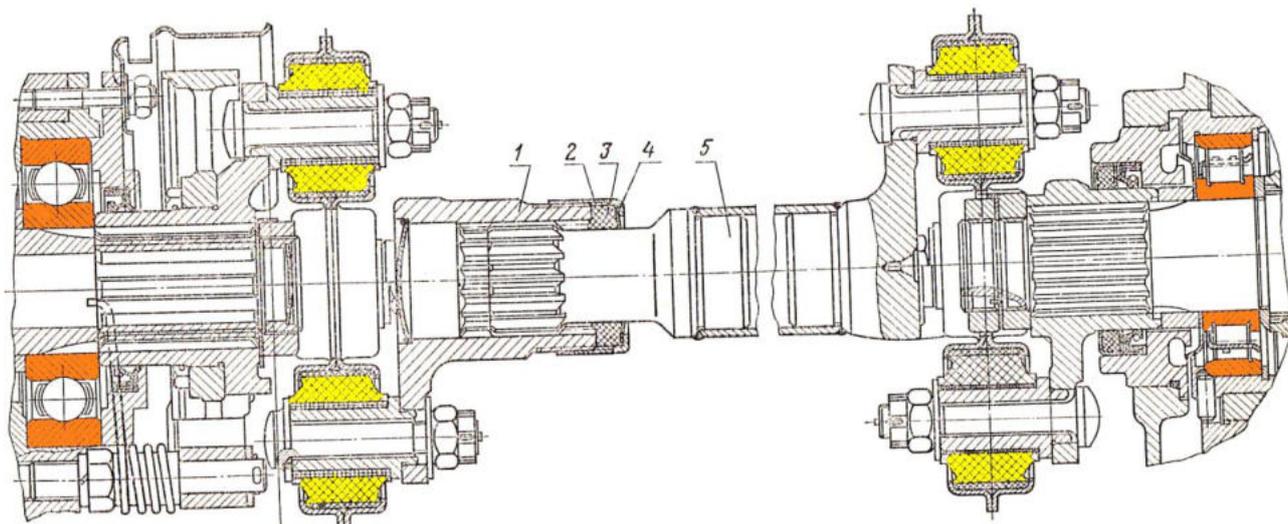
Карданная передача тракторов ДТ-75М, ДТ-75Б, ДТ-75К без УКМ, ходоуменьшителя и реверс-редуктора (продольный разрез):
